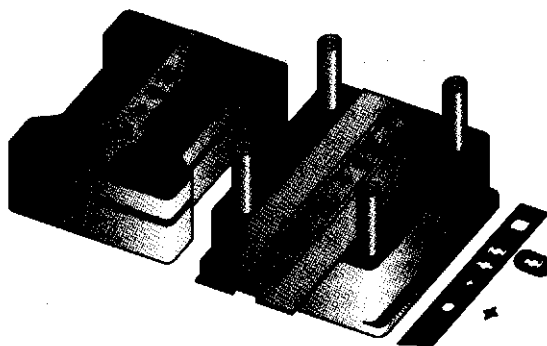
Армированный твердыми сплавами штамп для вырубки деталей из листовой стали для статоров и роторов электродвигателей
